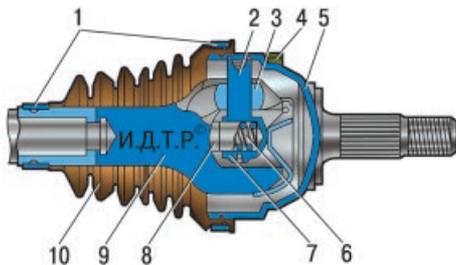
Наружный шарнир равных угловых скоростей: 1 – хомуты крепления чехла; 2 – трехшиповая ступица; 3 – ролик; 4 – зубчатый диск датчика ABS (при наличии ABS); 5 – корпус шарнира; 6 – пружина; 7 – регулировочная проставка; 8 – толкатель; 9 – вал привода; 10 – чехол шарнира
